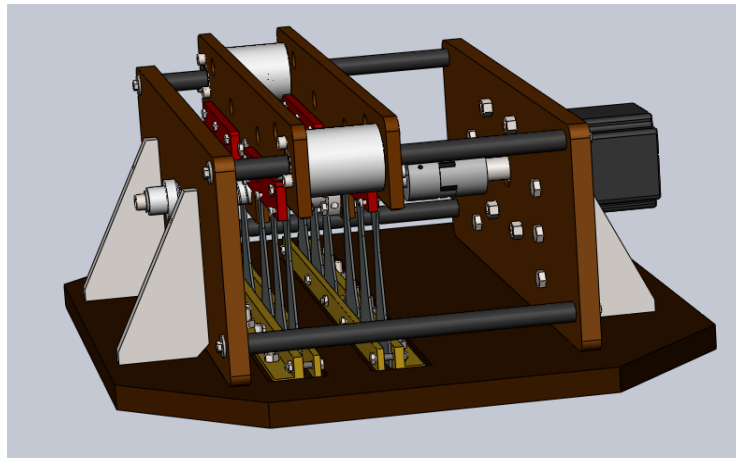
Assemblage Final de la machine sur SOLIDWORKS
